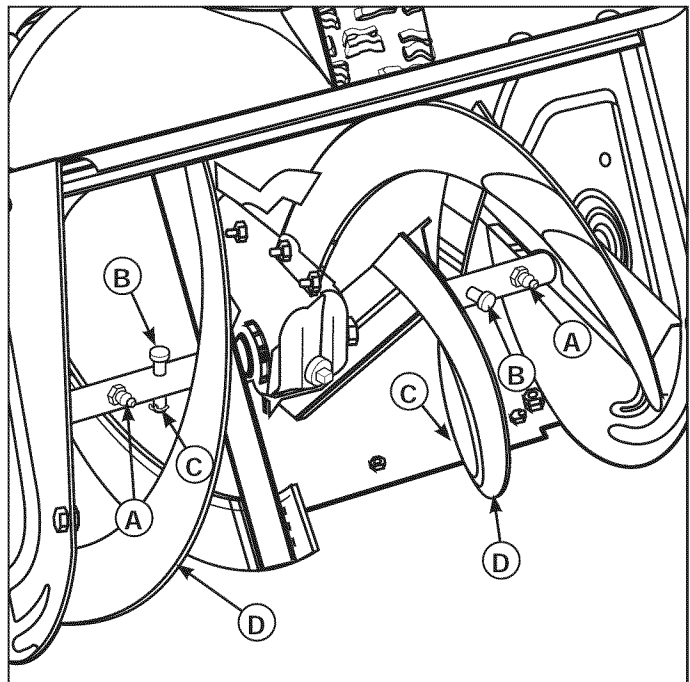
Lubricar el ensamblaje del eje del tornillo sinfín
